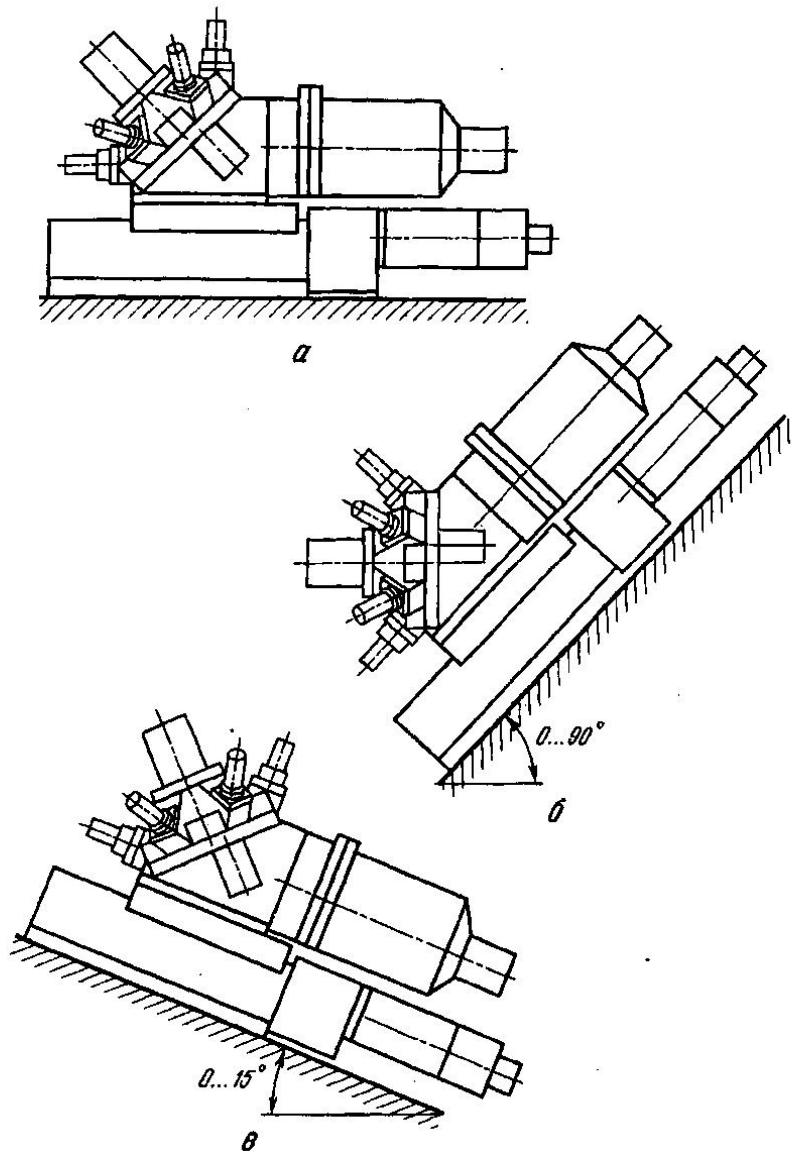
Варіанти установки револьверної бабки:
